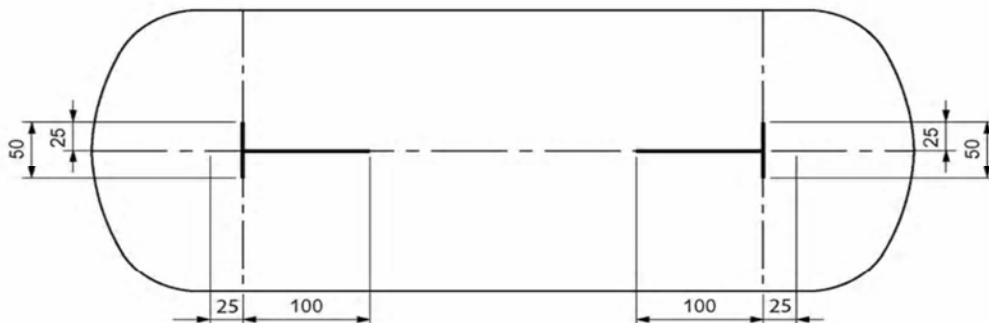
Extensión de la radiografía de las soldaduras. Botellas con soldaduras circunferenciales y longitudinales
